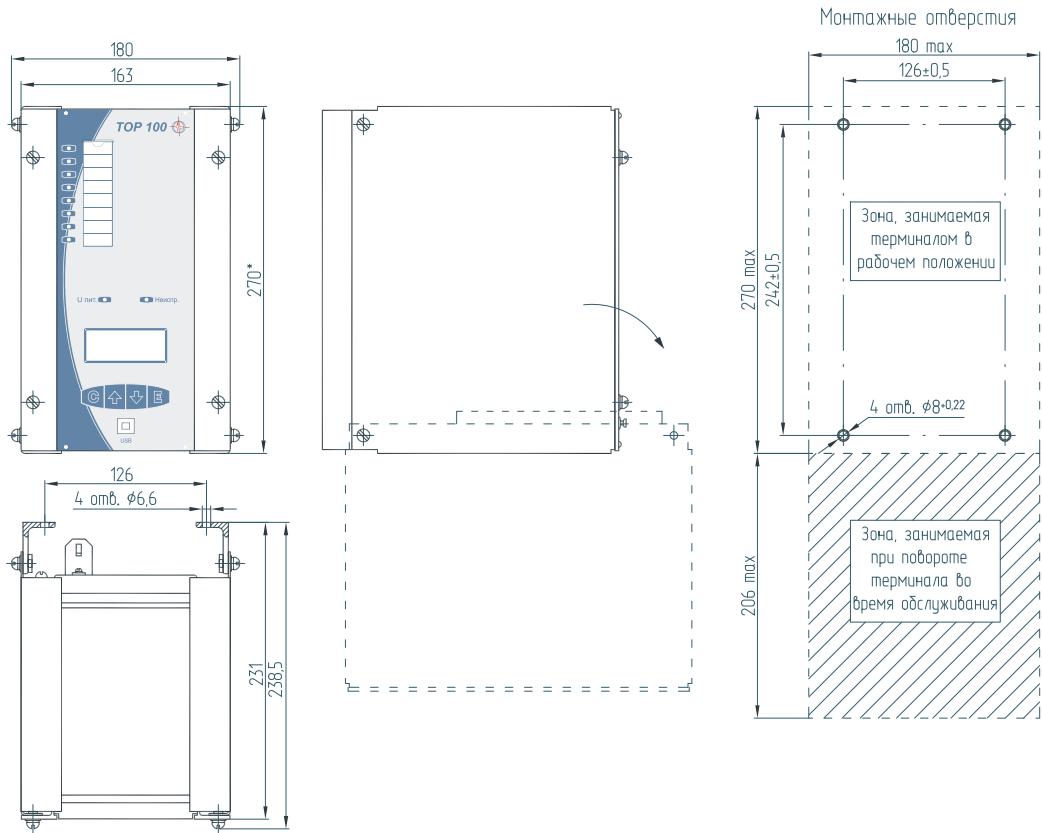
Габаритные и установочные размеры для навесного монтажа
